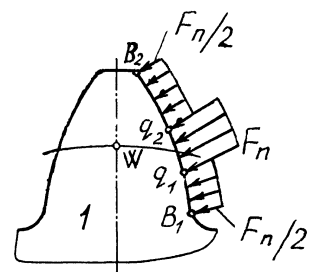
Цилиндрическая прямозубая зубчатая передача нарезанная без смещения режущего инструмента:
